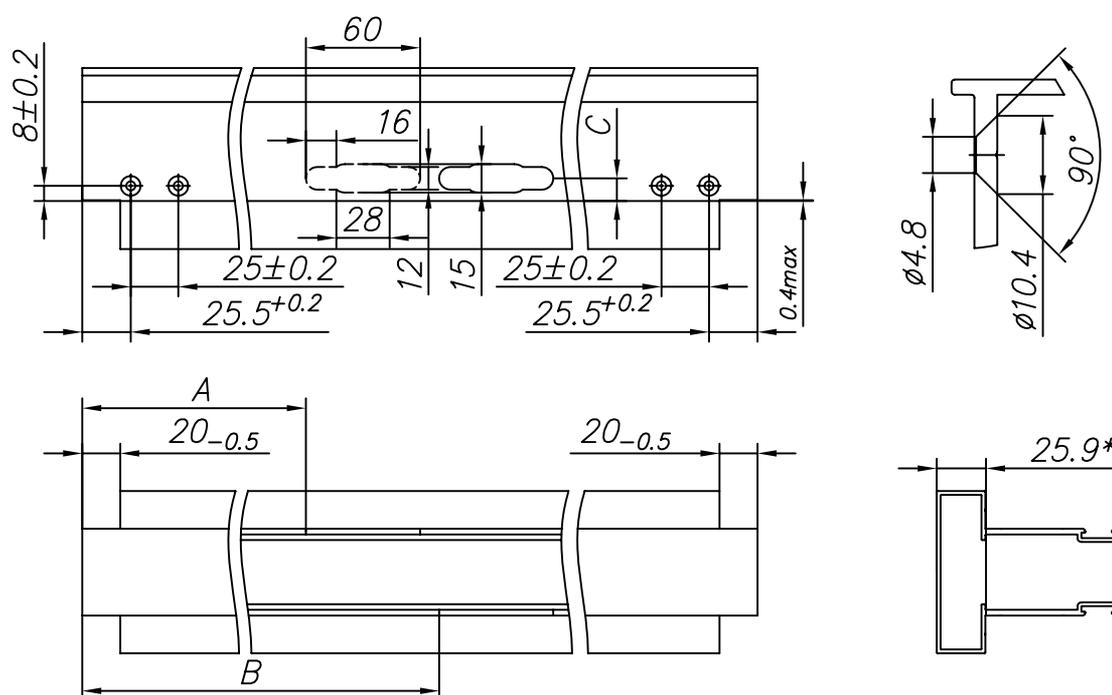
Изготовление импоста с пазами для тросовой растяжки
